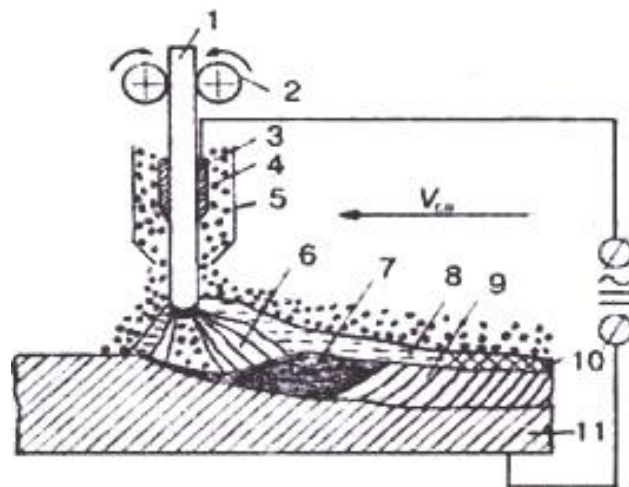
Схема автоматичного зварювання під флюсом: 1 – електрод; 2 – механізм подачі дроту; 3 – провідник струму; 4 – флюс; 5 – бункер; 6 – зварювальна дуга; 7 – зварювальна ванна; 8 – шлакова ванна; 9 – зварювальний шов; 10 – шлакова кірка; 11 – основний метал
